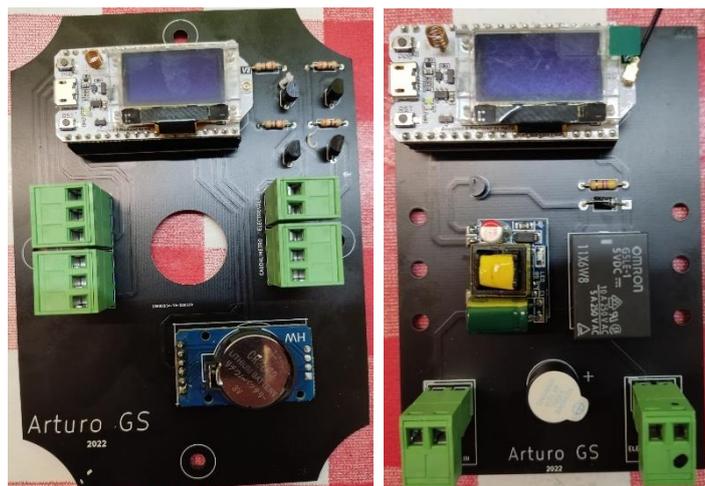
PCBs soldada. Fuente: elaboración propia.
